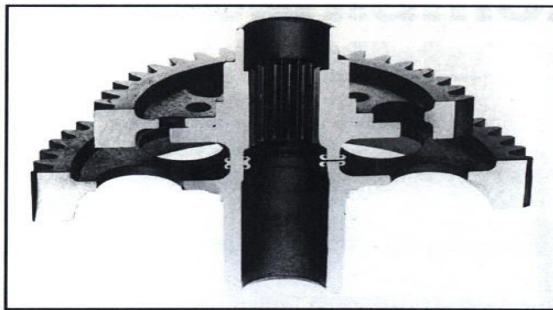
Soudage des roues dentées d'une boîte de vitesse [1].
